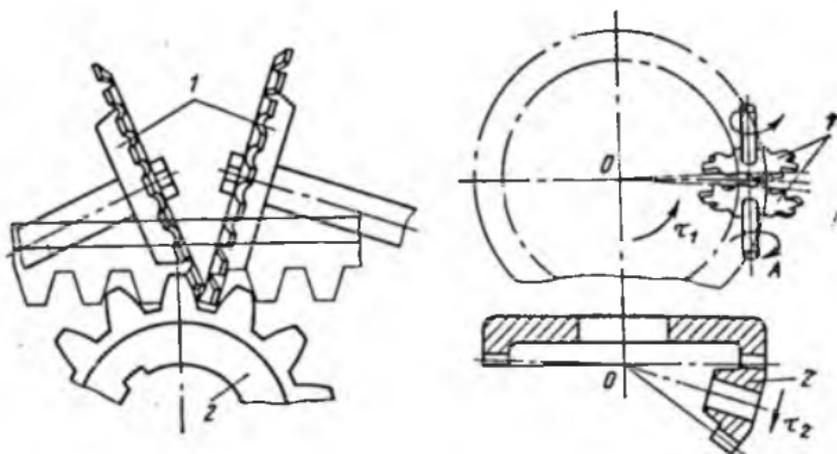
Нарезание конических зубчатых колес дисковыми фрезами
